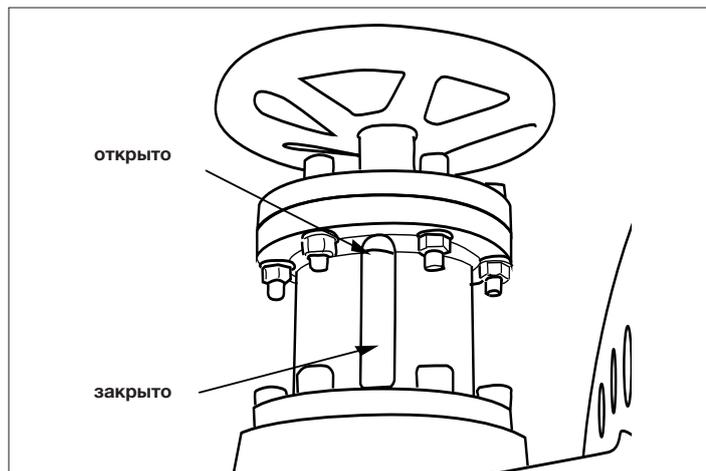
VAG EKN® Поворотный затвор с UVV-блокировкой
